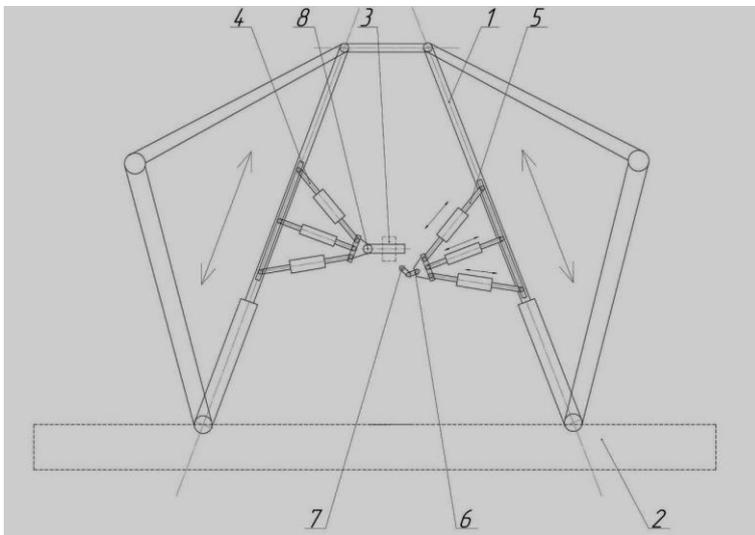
Схема обработки зубчатого колеса с применением станка-робота
